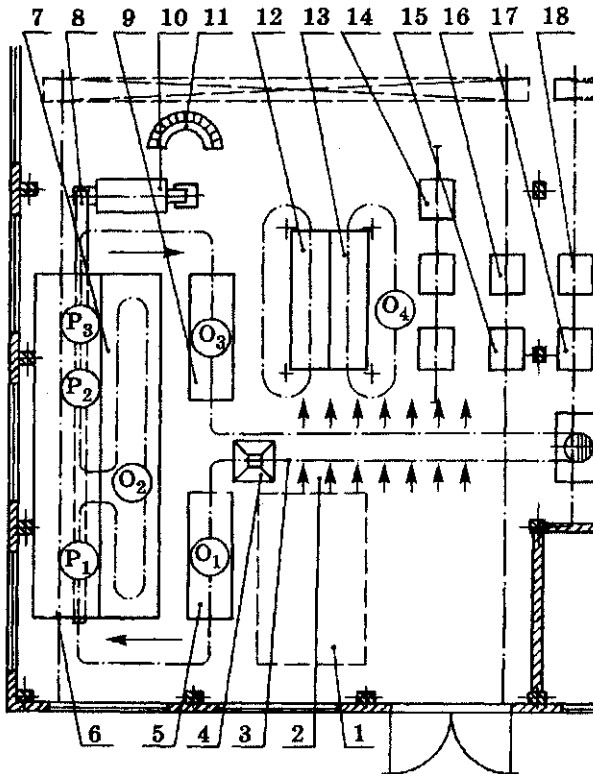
Планировка разборочно-очистного участка двигателей:
